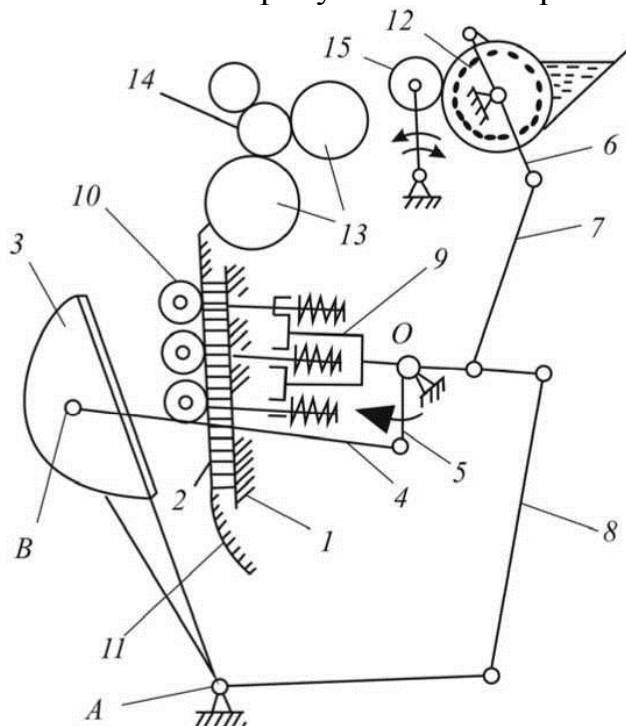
Кинематическая схема тигельной машины легкого типа: 1 - талер; 2 - форма; 3 - тигель; 4 - шатун; 5 - кривошип; 6-8 - рычаги; 9 - каретка; 10 - накатные валики; 11 - направляющие; 12 - дукторный цилиндр; 13 - раскатные цилиндры; 14 - раскатной валик; 15 - передаточный валик
